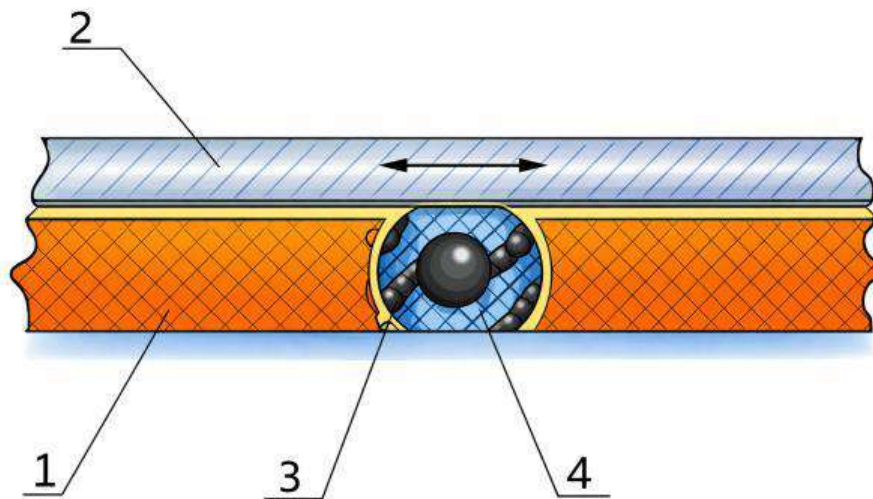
Схема самозмащувального підшипника ковзання
